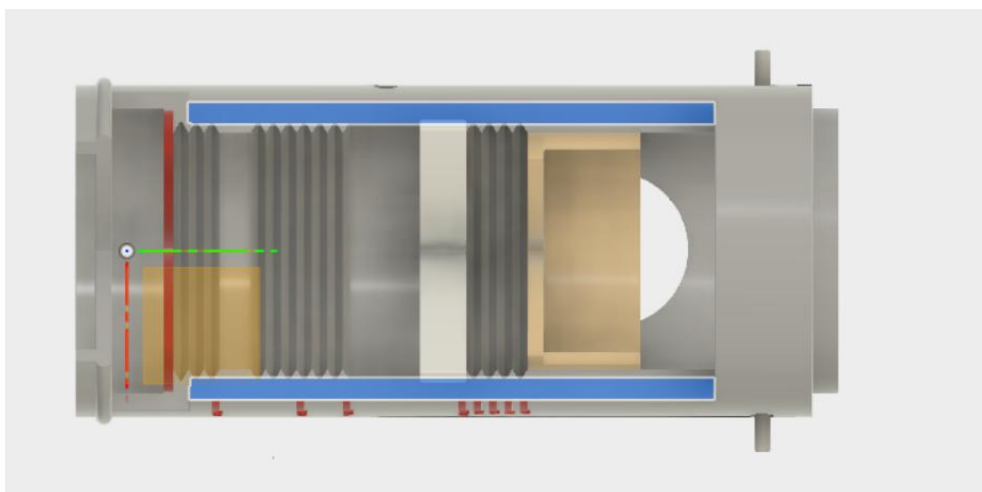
Отверстие в корпусе, обеспечивающее доступ к внутренней части
